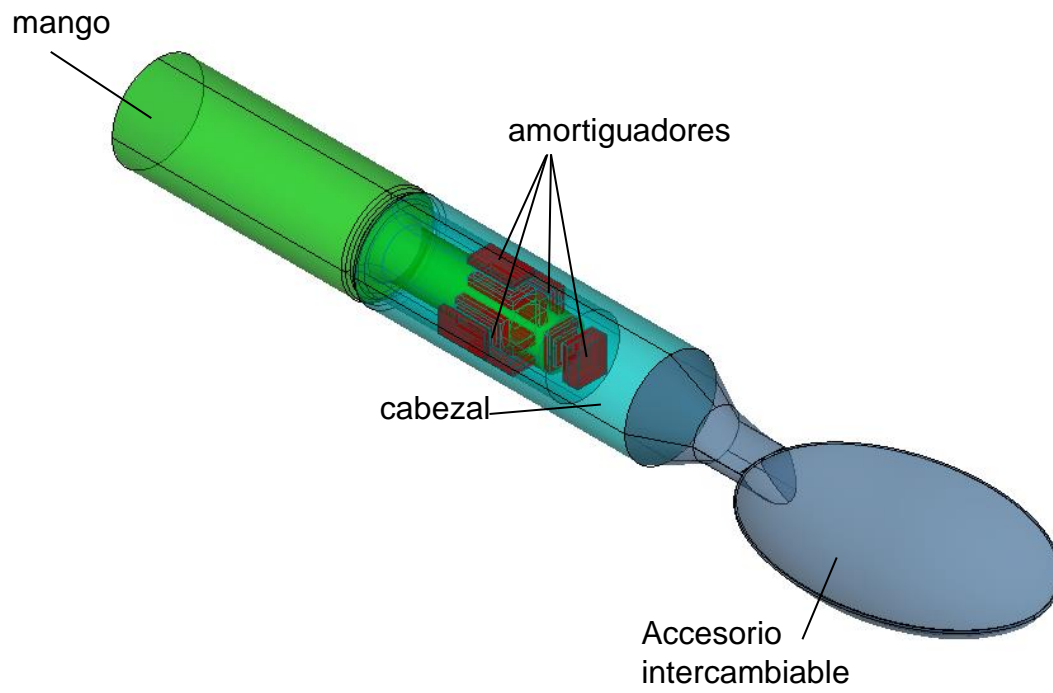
Detalles Diseño 5. Fuente: Elaboración propia
